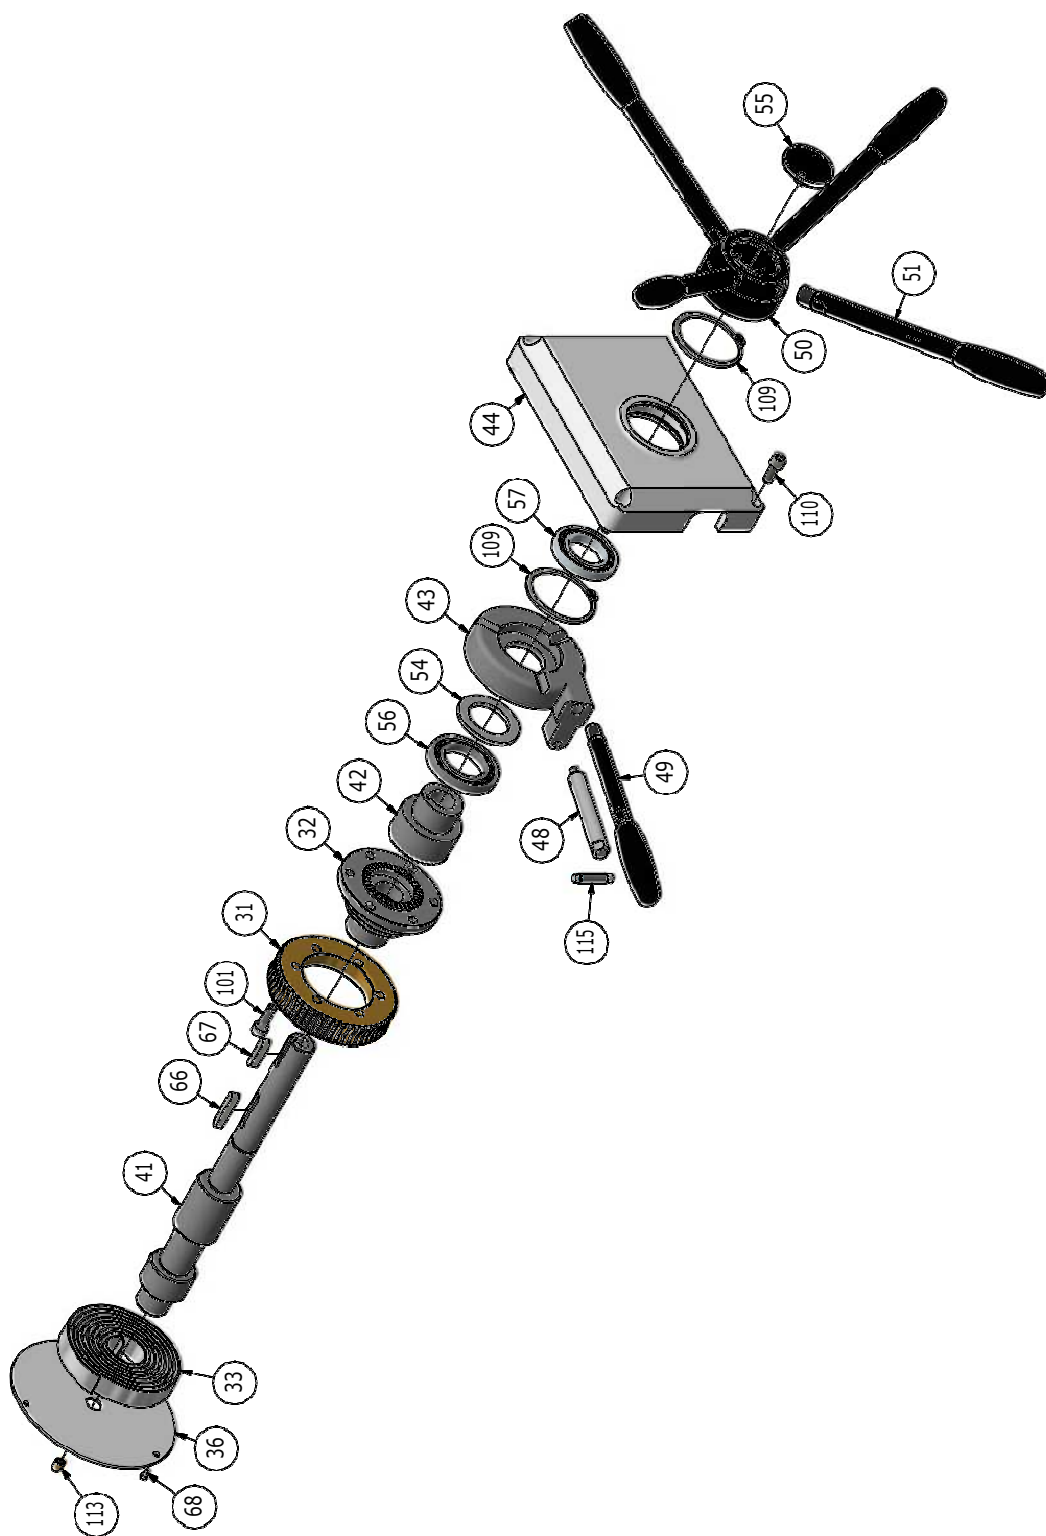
GetriebeTeilB - Elemento de engranajeB
